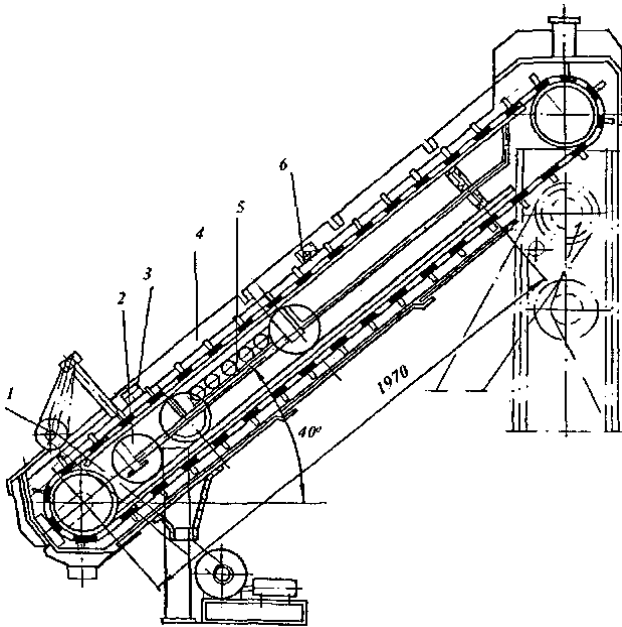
Стрічковий шпарник БКП-200: 1 – шнек; 2 – стрічка із дротяної сітки; 3, 6 – ополіскуючі пристрої; 4 – корпус; 5 – труби.
